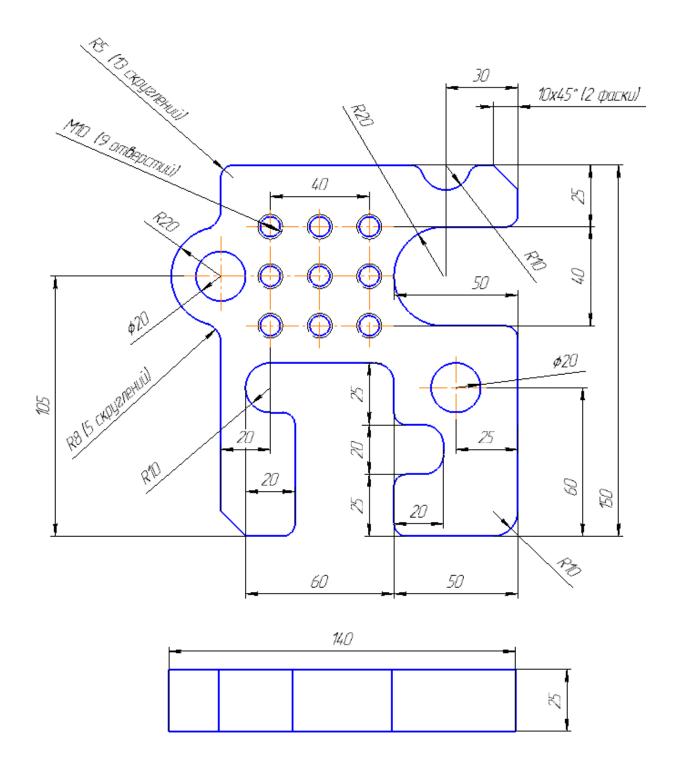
Чертеж детали (материал: Алюминий ДТ16).
